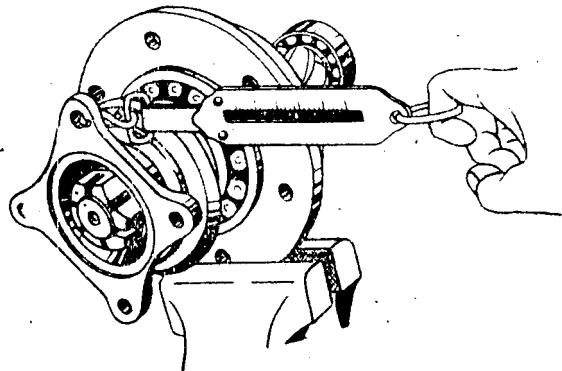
Проверка затяжки подшипников ведущей шестерни.
